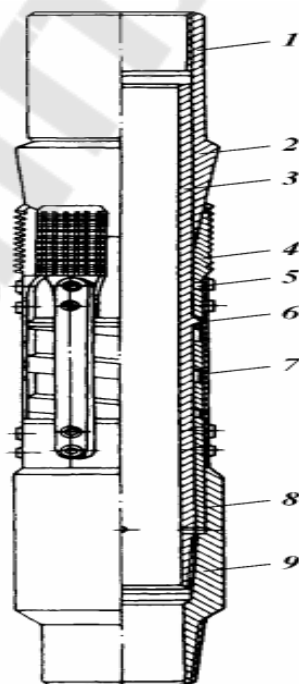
Клиновое подвесное устройство гидравлического действия: 1 – обсадная труба; 2 – конусообразная муфта; 3 – корпус; 4, 7 – верхнее и нижнее кольца центратора; 5 – штифт; 6 – пружинная планка центратора; 8 – поршень; 9 – соединительная муфта
